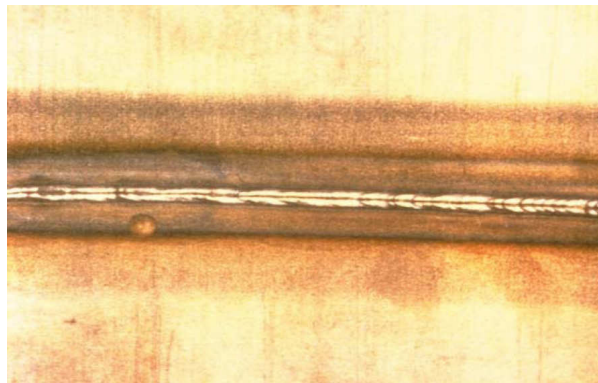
Zona termicamente afetada (ZTA) devido ao processo de soldagem.
